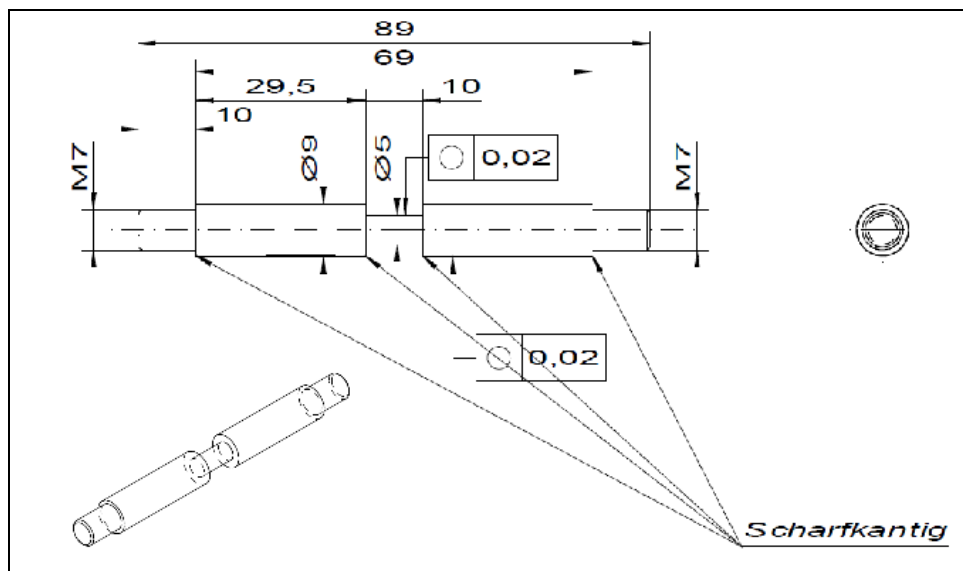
Abmessungen der für den Adapter benötigten Zugproben [9]
